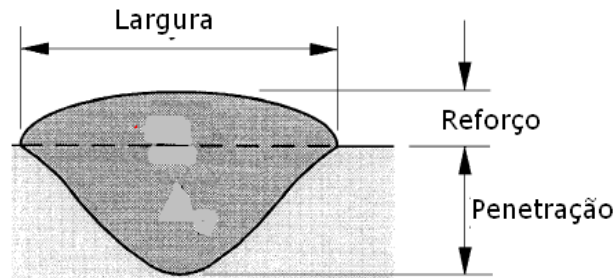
Desenho esquemático das dimensões do cordão de solda
